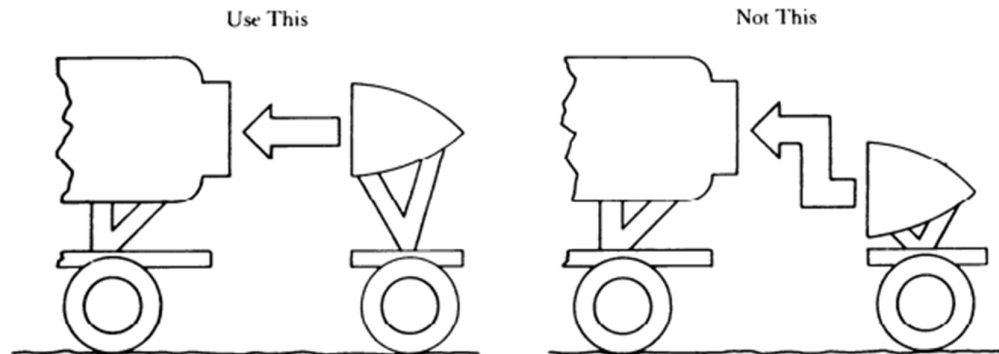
Esempio attrezzatura smontaggio e assemblaggio
